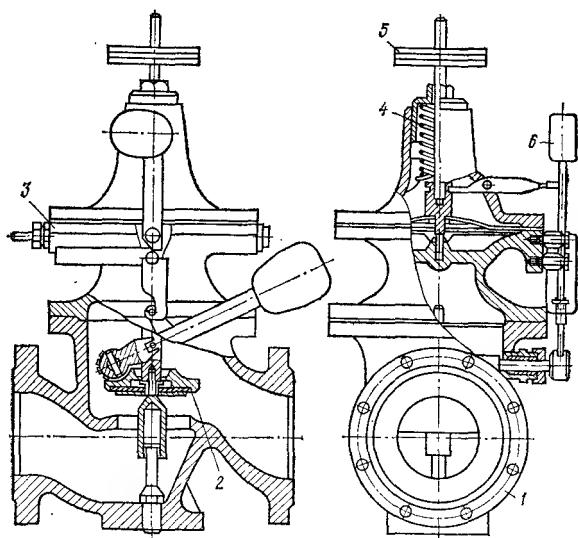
Малогабаритный предохранительный запорный клапан типа ПКН (ПКВ)
